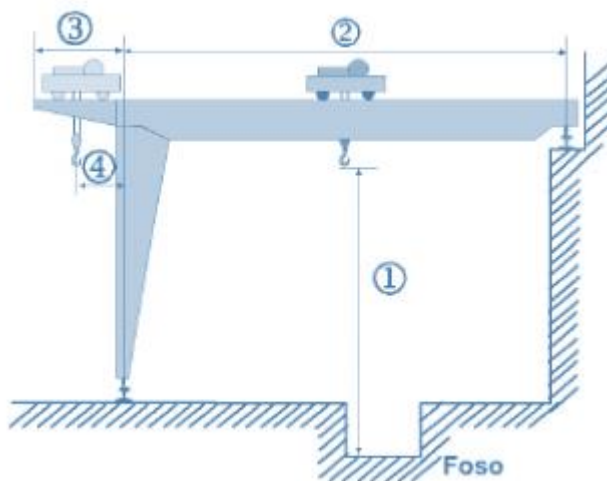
Parámetros de un puente grúa – Fuente: NTP 736
